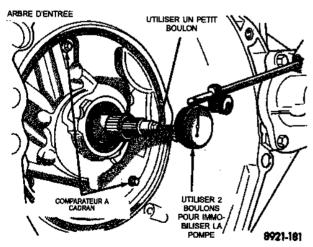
Mesure du jeu axial de l'arbre d'entrée
